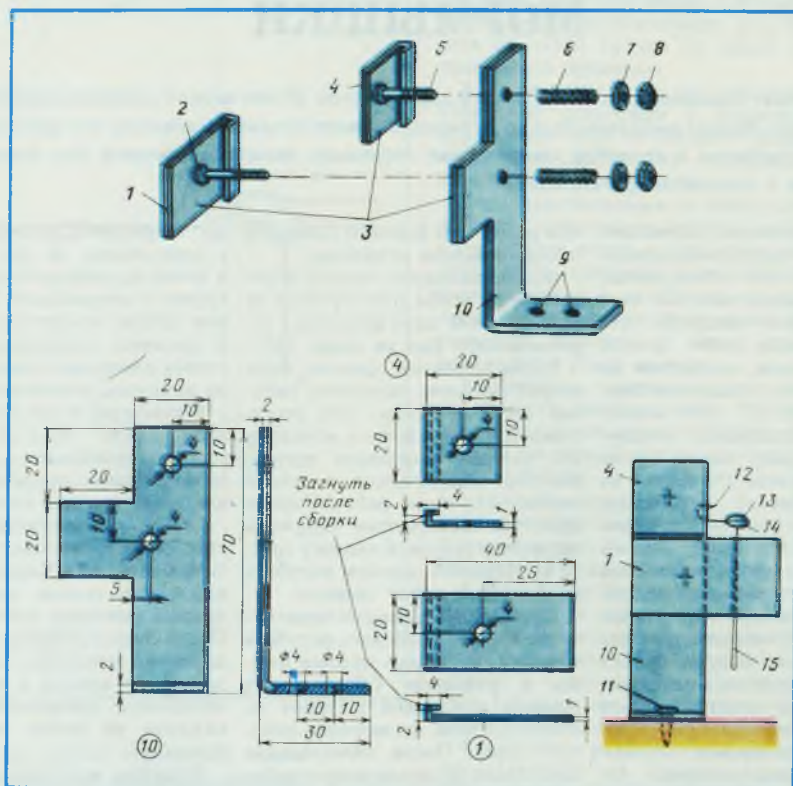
Кондуктор для пайки мормышек (сборочный чертеж и детали): 1 — прижим иглы (медь, латунь); 2 — головки винтов; 3 — наждачная бумага (резина); 4 — прижим крючка (медь, латунь); 5 — винт М3×20; 6 — пружина; 7 — шайба; 8 — гайка М3; 9 — отверстия для крепления стойки; 10 — алюминиевая стойка; 11 — крепление кондуктора; 12 — крючок; 13 — припой; 14 — чешуйка; 15 — титановая игла.
